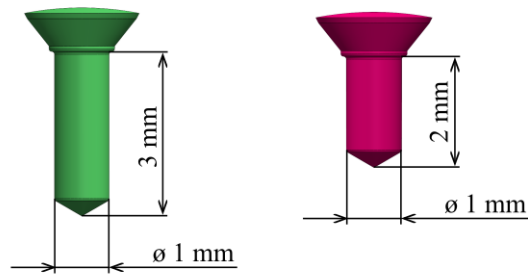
Model geometrie fixátoru s hlavními rozměry
